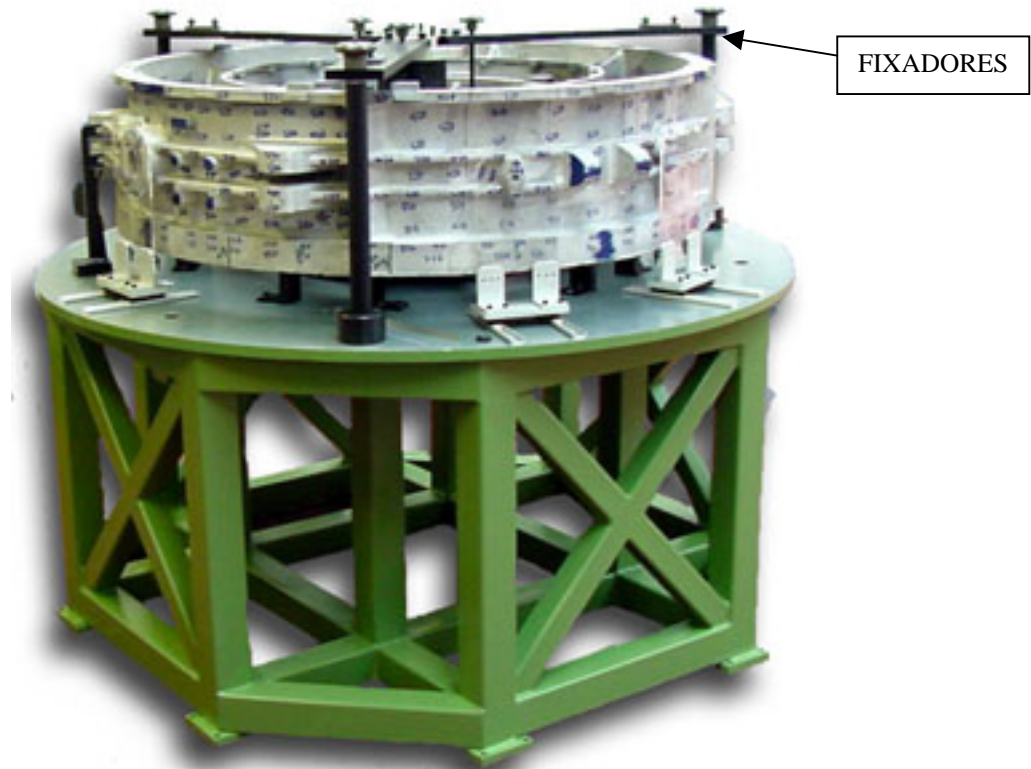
dispositivo de fixação para soldagem da parte de uma aeronave
